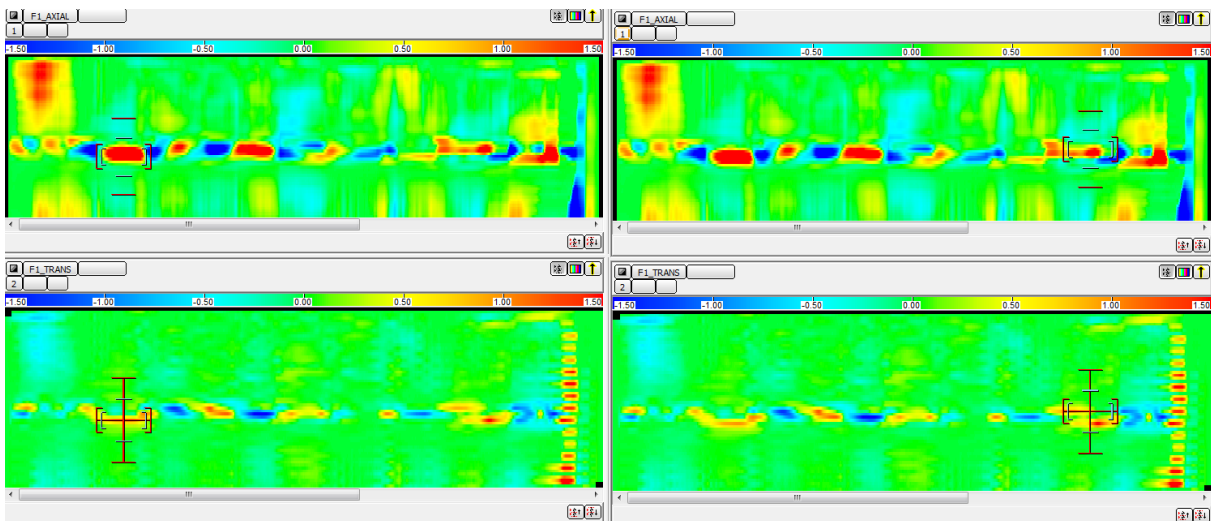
ET vzorku č. 8 se zaměřením obou trhlin
